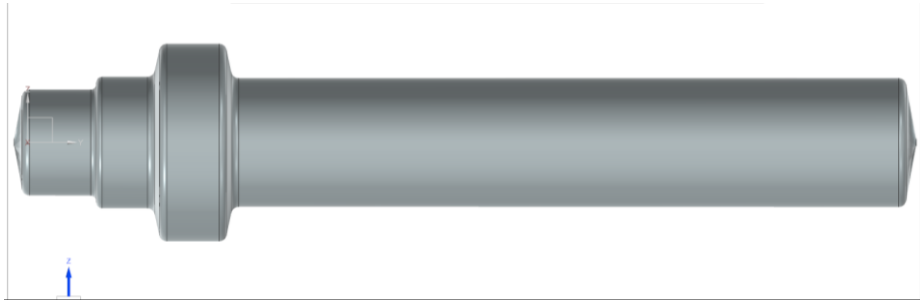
3-D модель заготовки отриманої на КГШП
